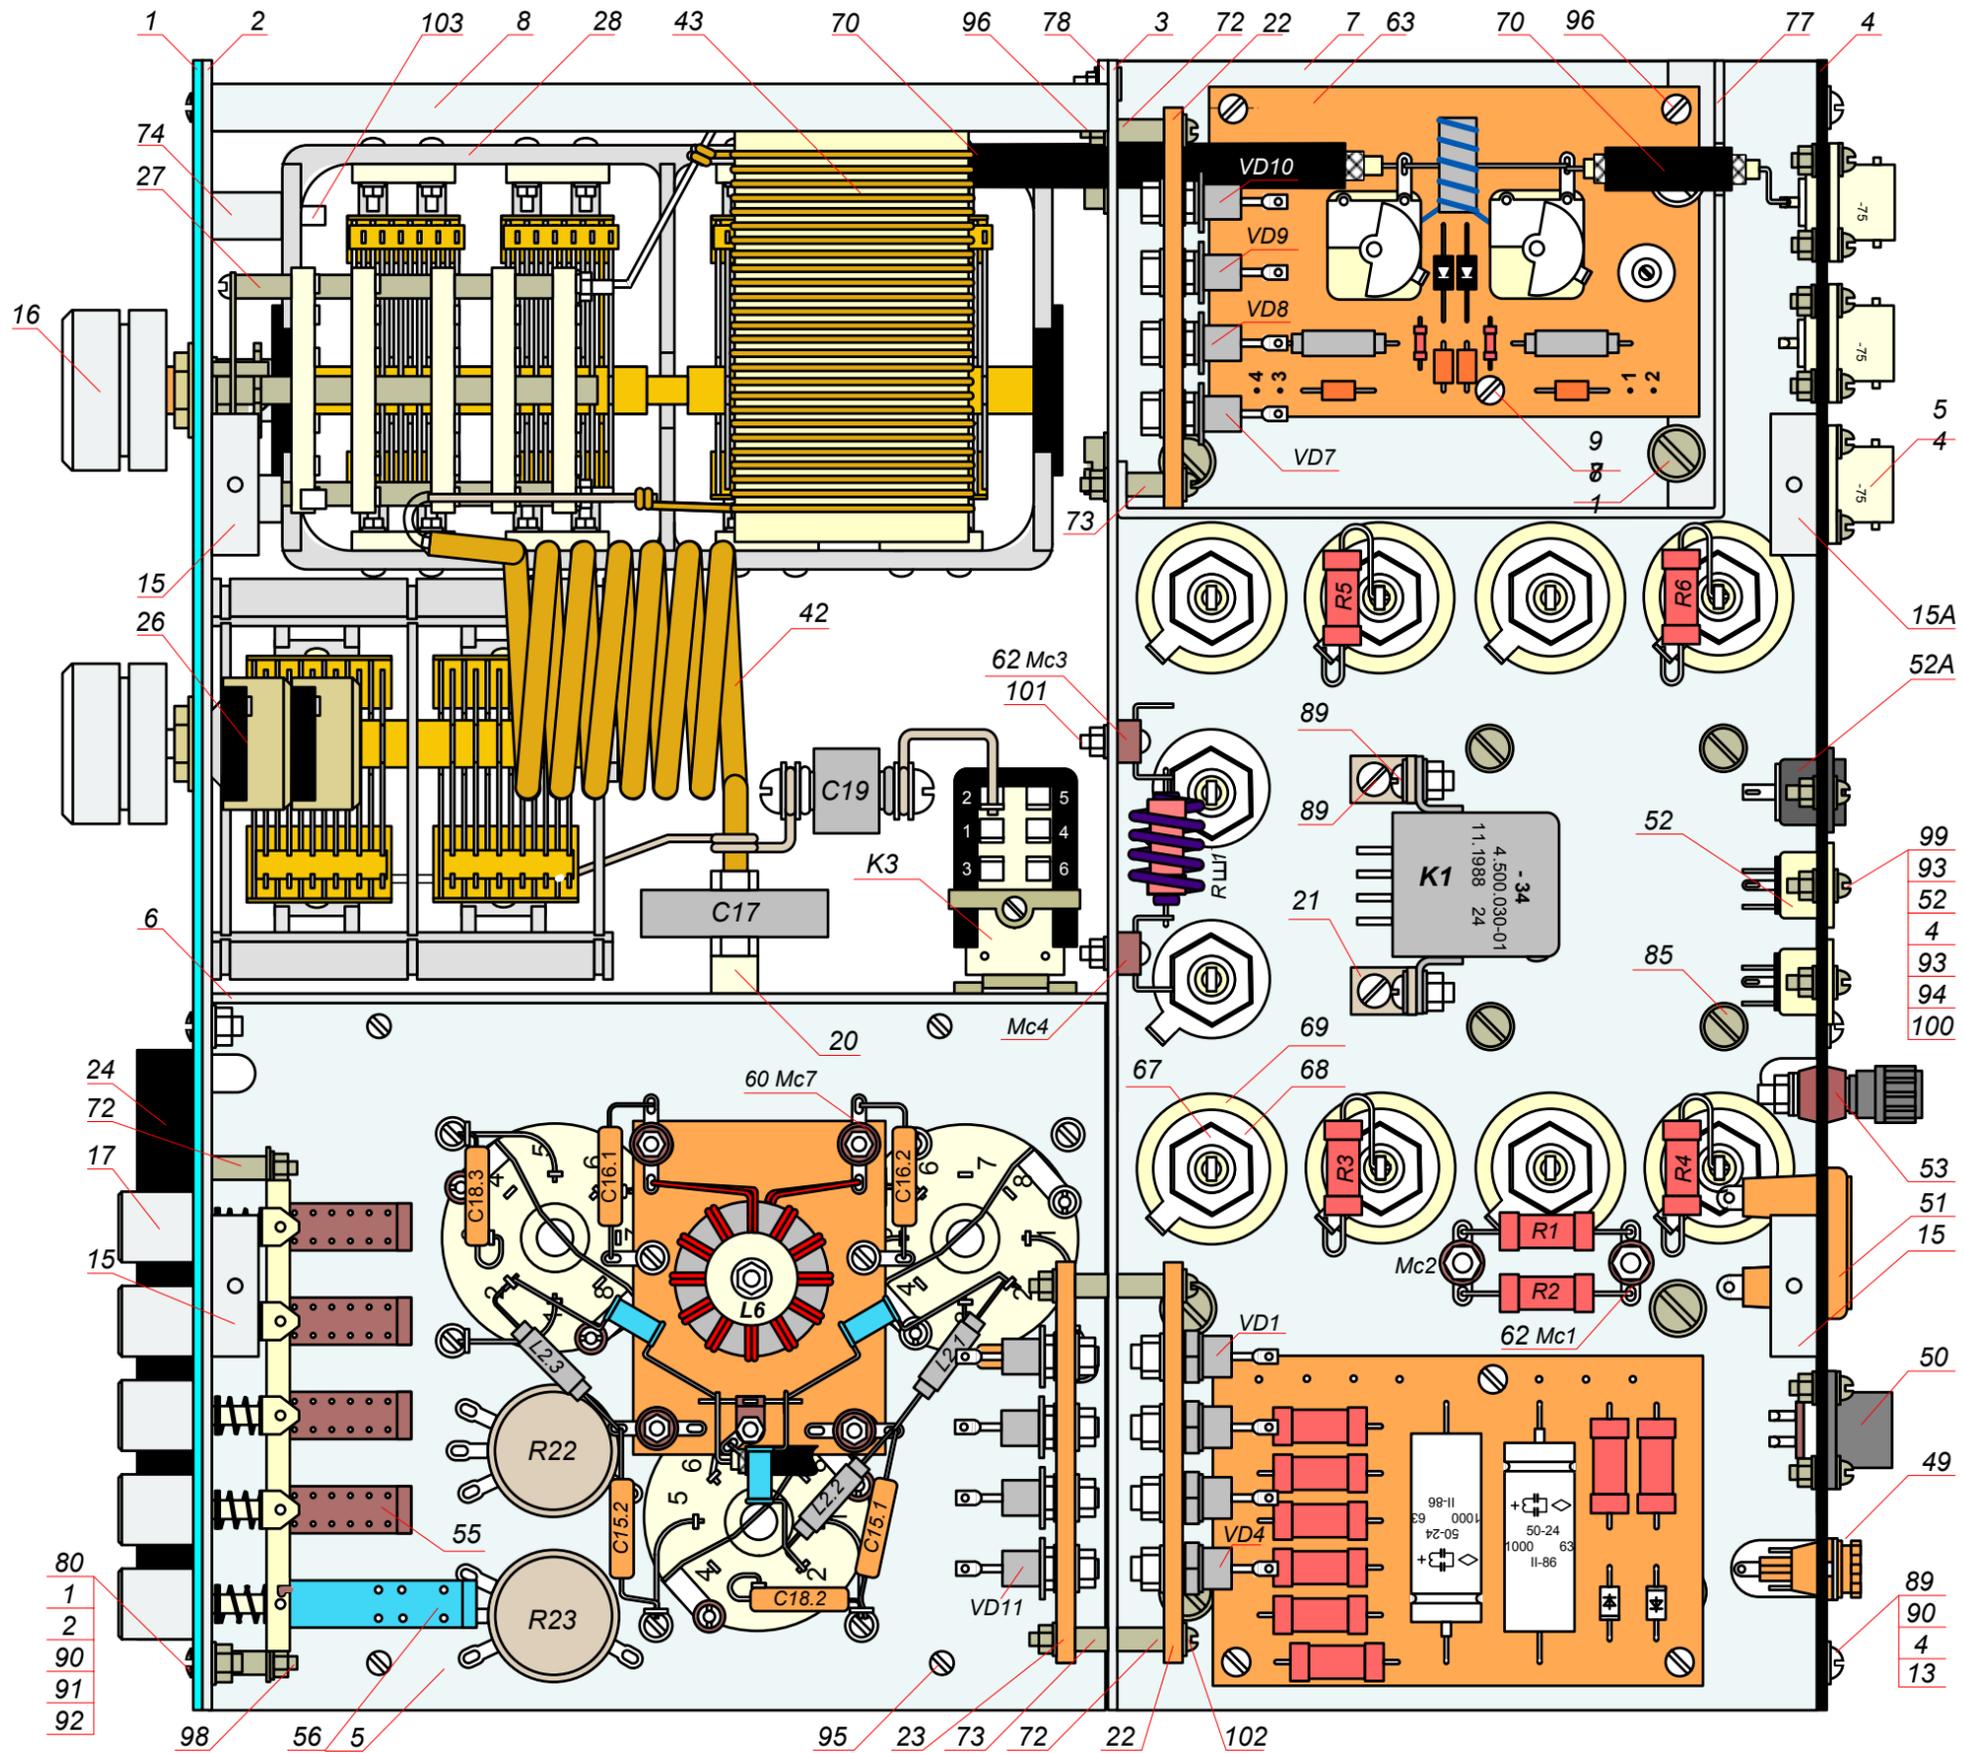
F. Сборочный чертёж усилителя DVA-300F (3 ГУ-50). Вид сверху со снятой верхней крышкой.
